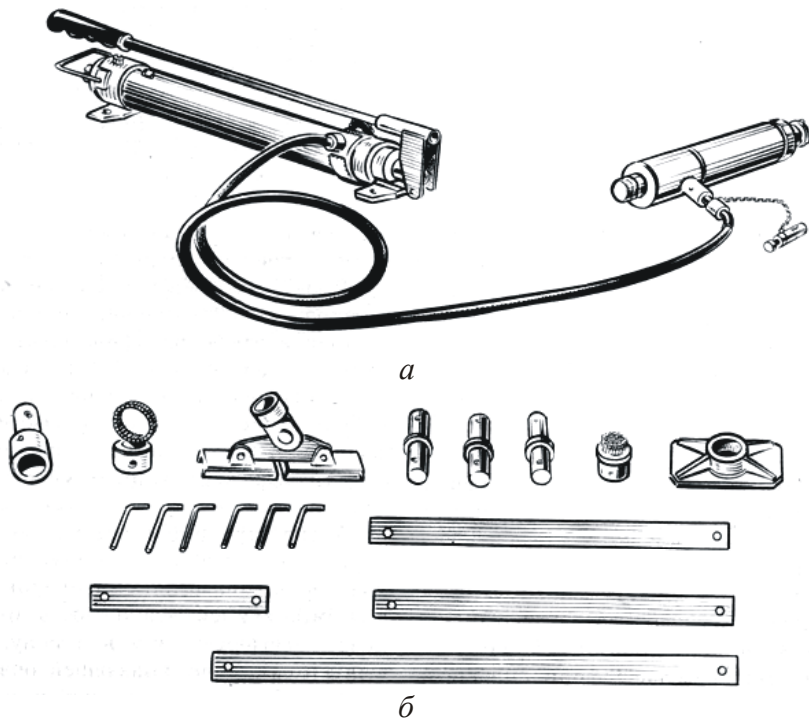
Оснастка для правки кузовов: *а* – гидравлическое устройство; *б* – набор приспособлений
